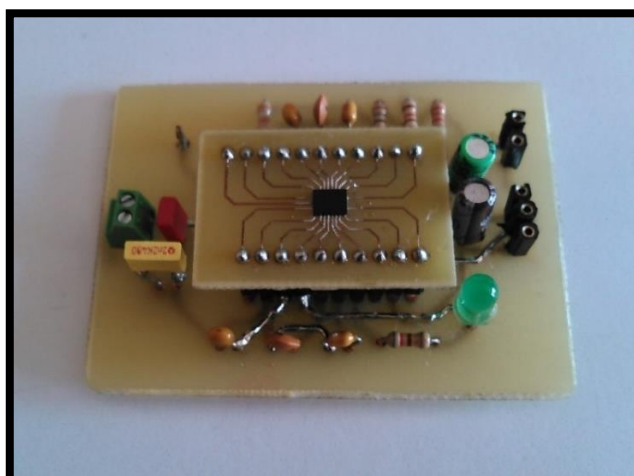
PCB del circuito del chip bq51050B con el zócalo conectado
